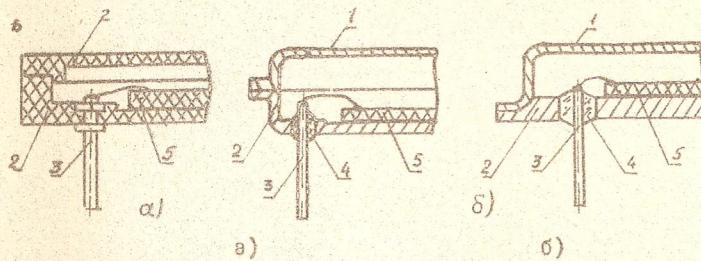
Пластмассовый (а) и металлокстеклянное (б) корпуса:
